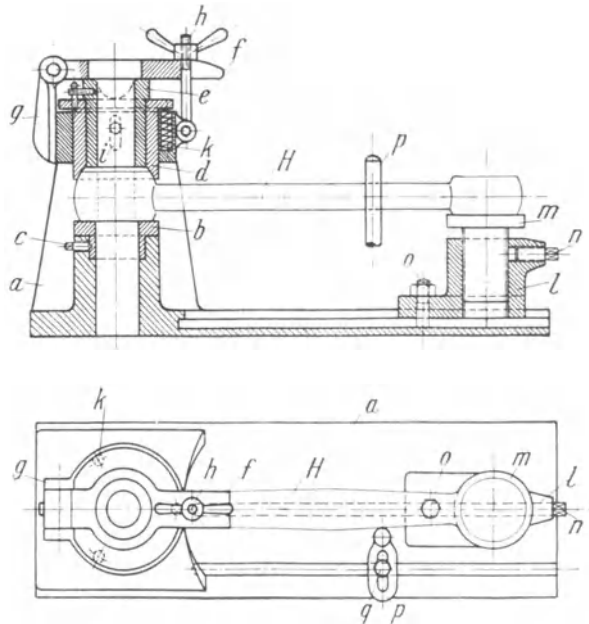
Bohrvorrichtung zum Bohren der Augen an Pleuelstangen.
